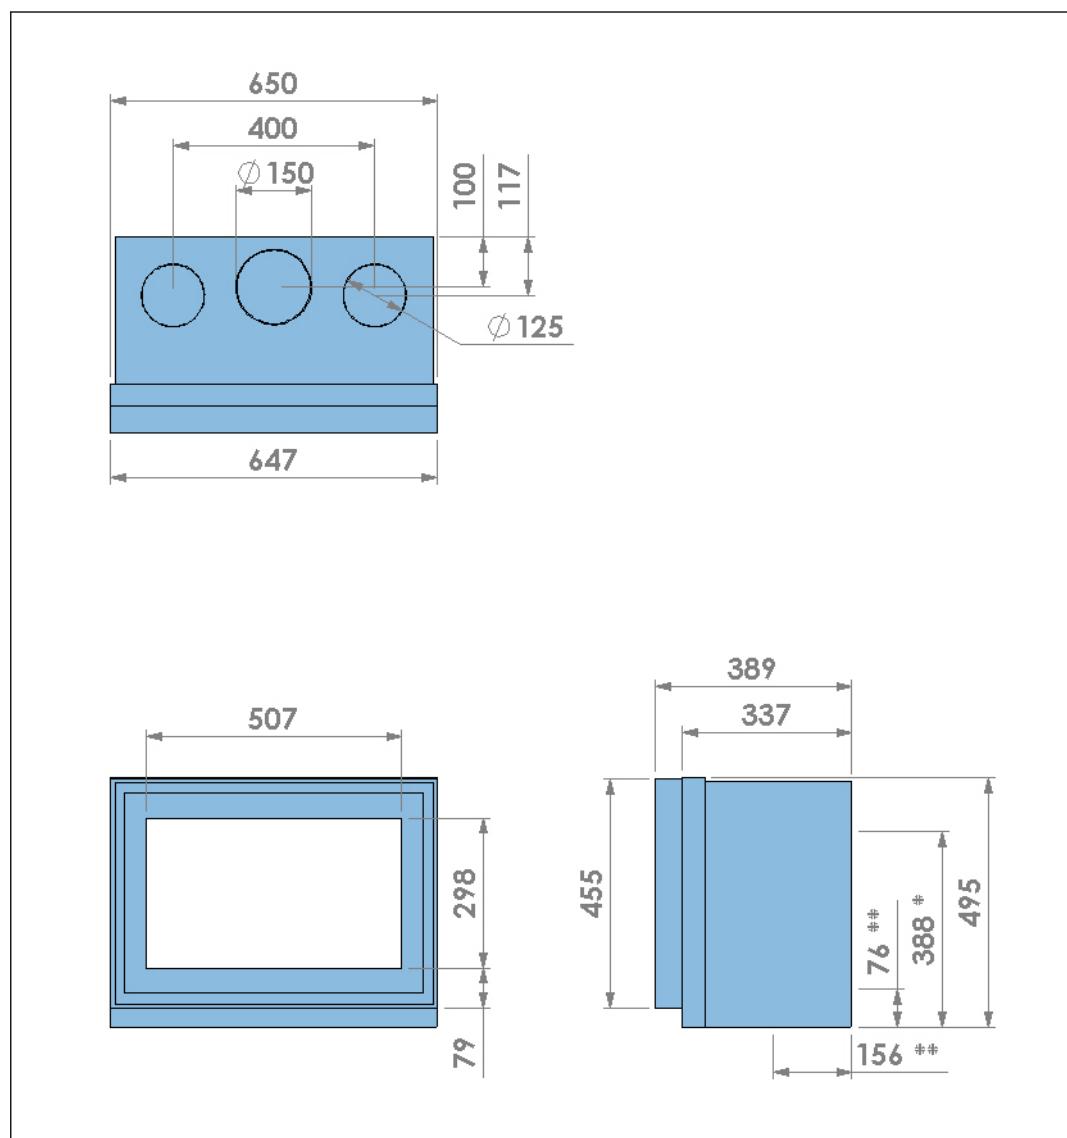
Dimensions d'appareil avec châssis intégré et porte à châssis en métal
